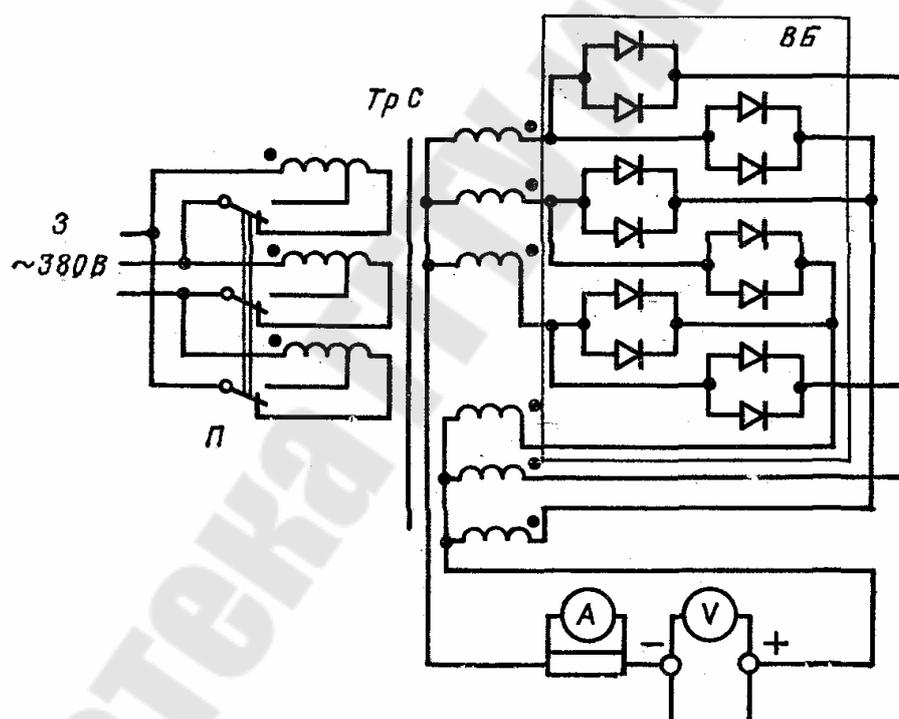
Электрическая схема силовых блоков сварочного выпрямителя ВКСМ-1000.
